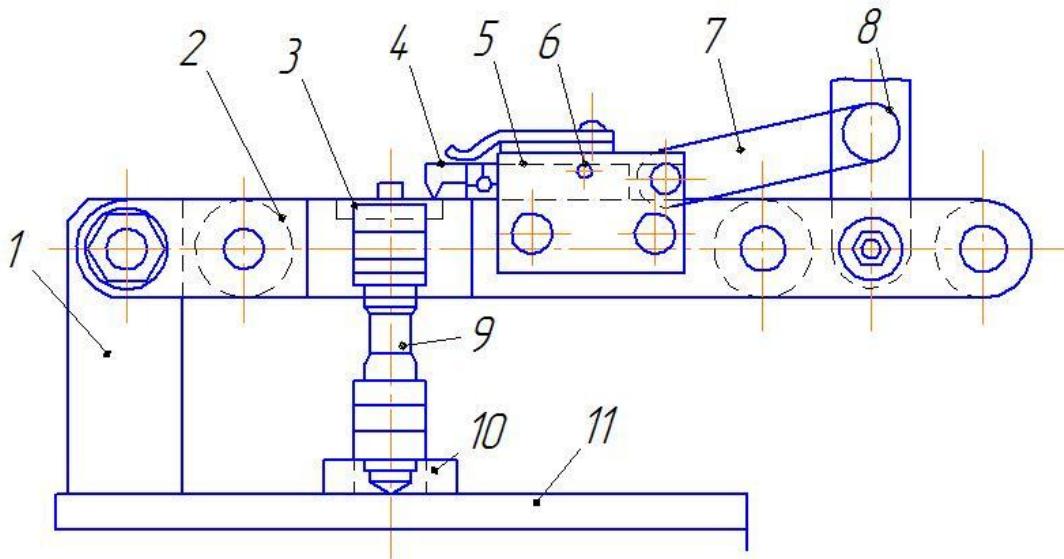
Приспособление для разборки и сборки подшипникового узла нажимного валика прядильной машины:
